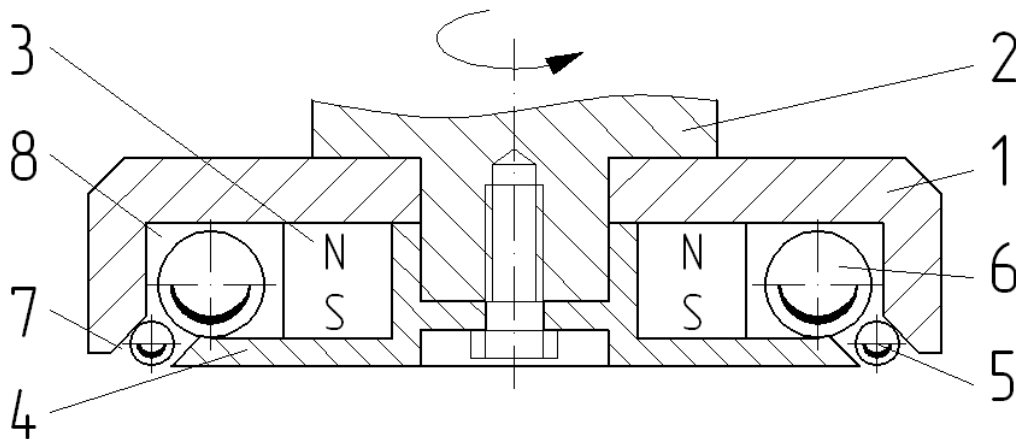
Двухрядный инструмент для магнитно-динамического упрочнения плоских поверхностей
